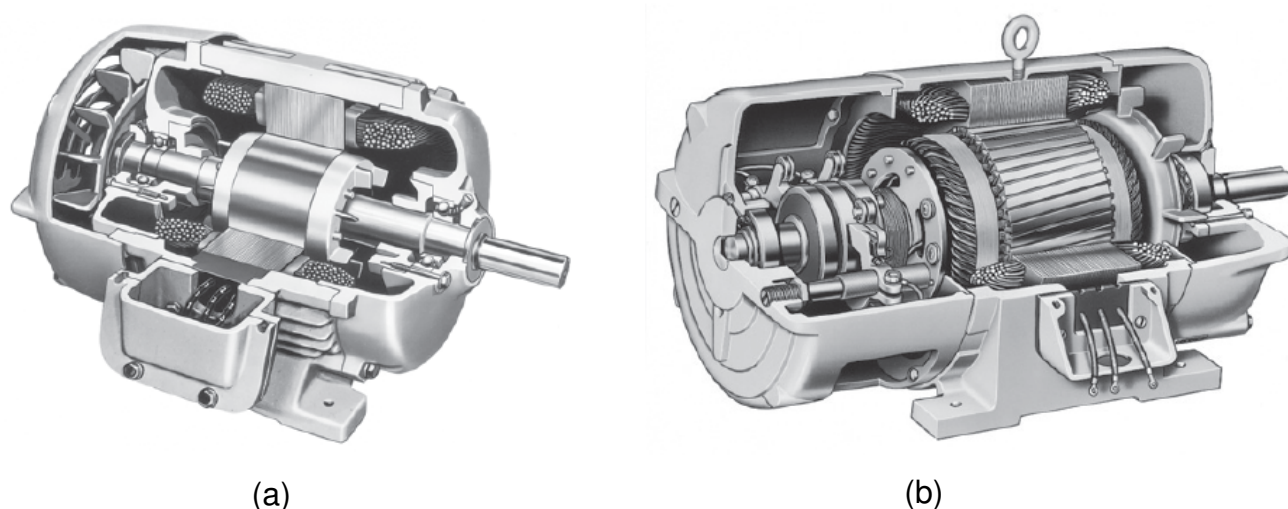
Motor de Indução Trifásico do tipo (a) rotor em gaiola de esquilo e (b) rotor bobinado.
